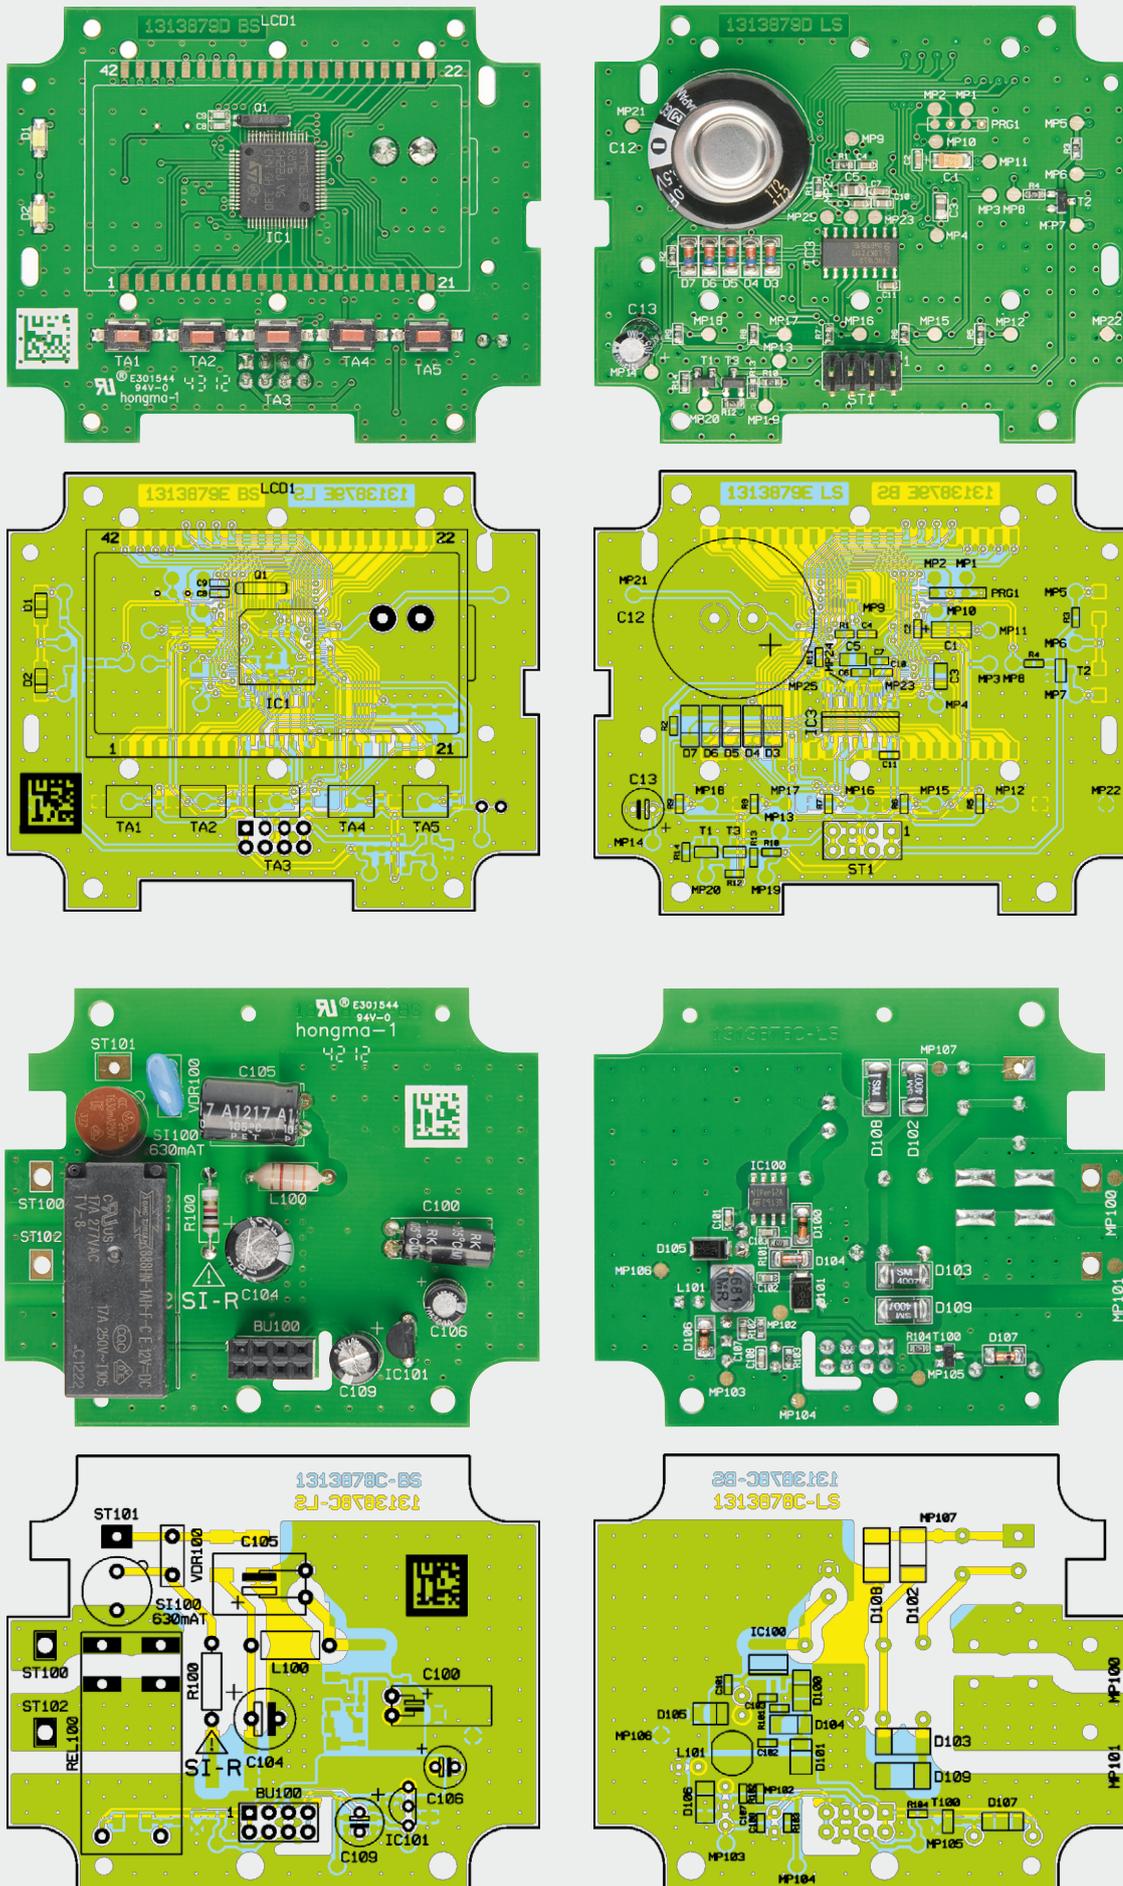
Fertig bestückte Platinen des WTA100 mit zugehörigen Bestückungsplänen, oben die Displayplatine, unten die Netzteilplatine
